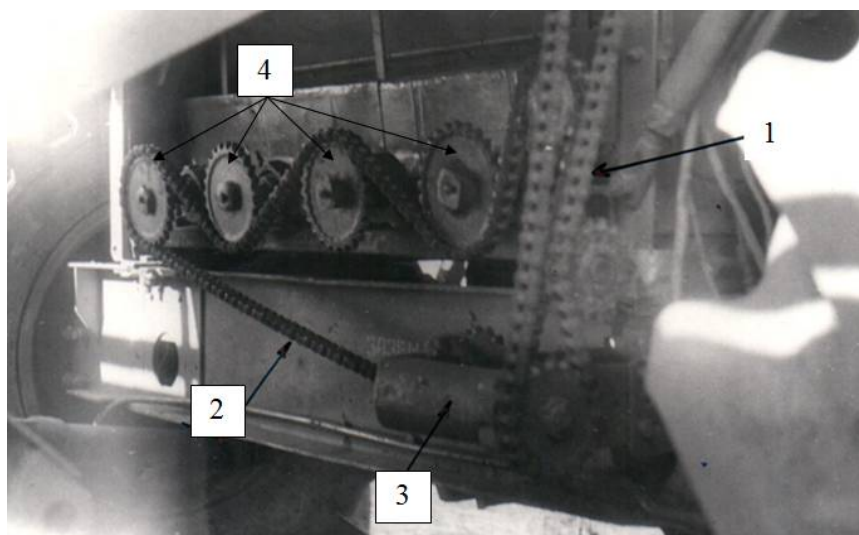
Привод шнеков: 1,2 – цепь; 3 – конический редуктор; 4 – звёздочки
